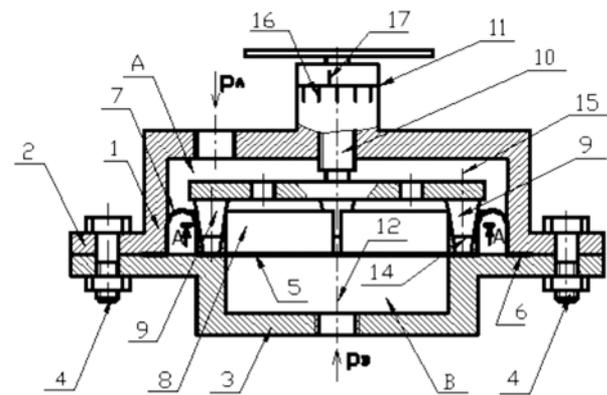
Мембранный узел с несколькими коническими сухарями
